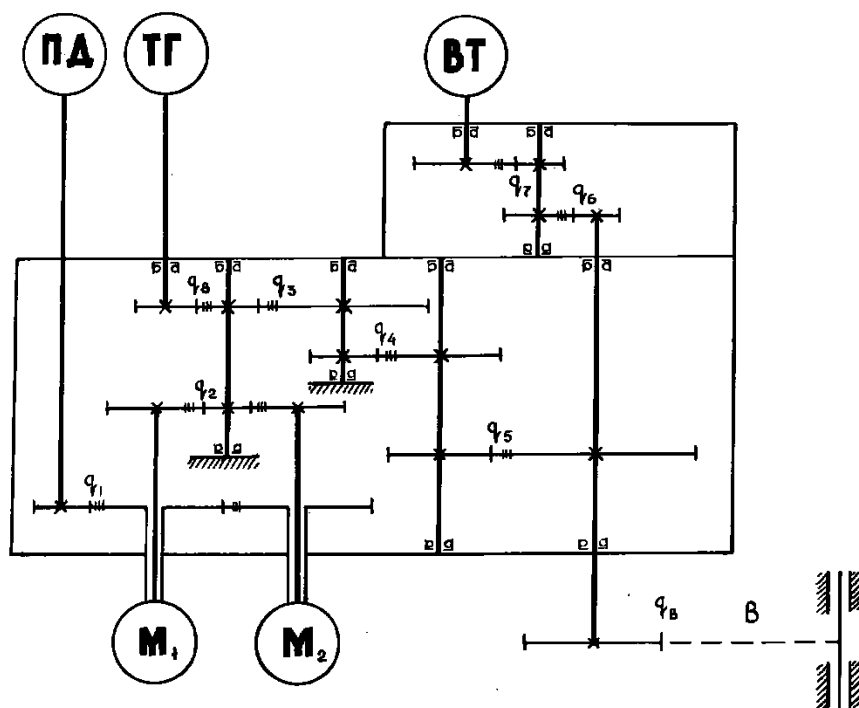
Кинематическая схема редуктора ЭСП с электромагнитными муфтами
